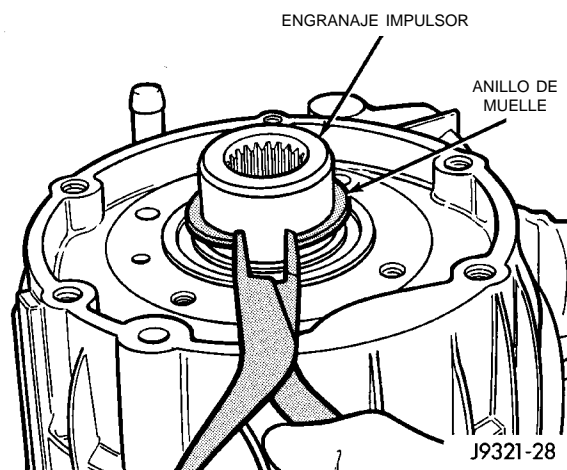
Desmontaje del anillo de muelle del engranaje impulsor
